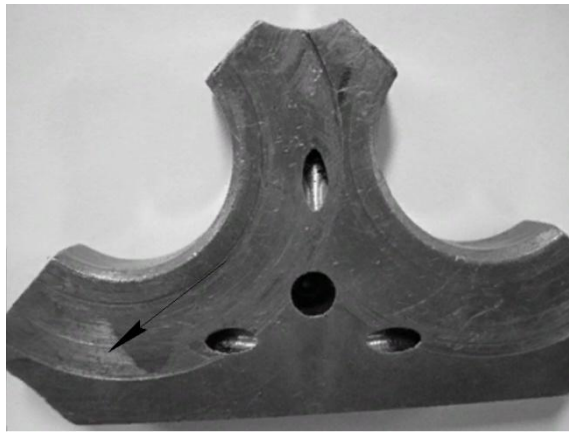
Зовнішній вид зносу торцевої поверхні платика насоса
